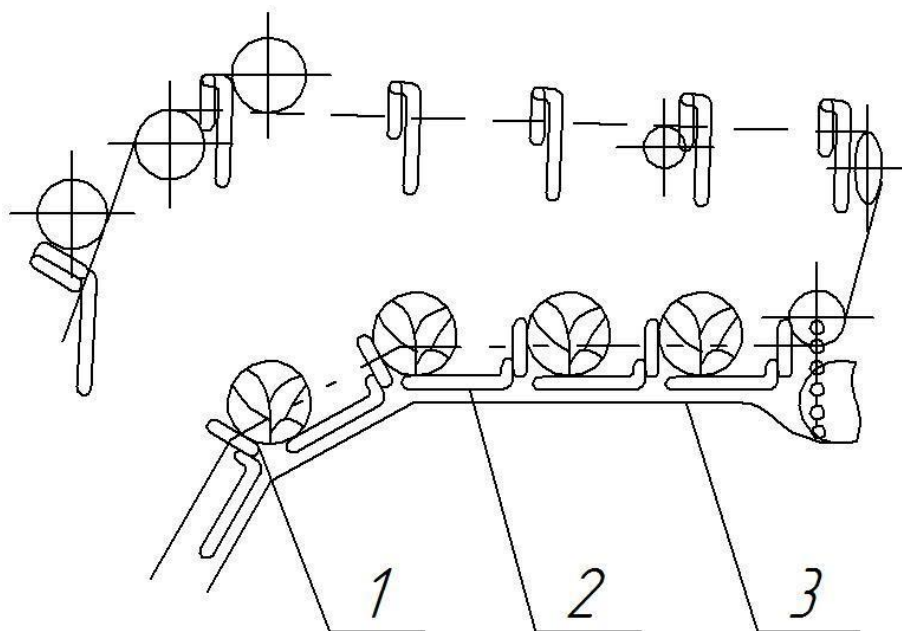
Схема скребкового елеватора з нижньою гілкою транспортування: 1 - транспортувальна пластина, 2 - скребок, 3 - сталевий настил
